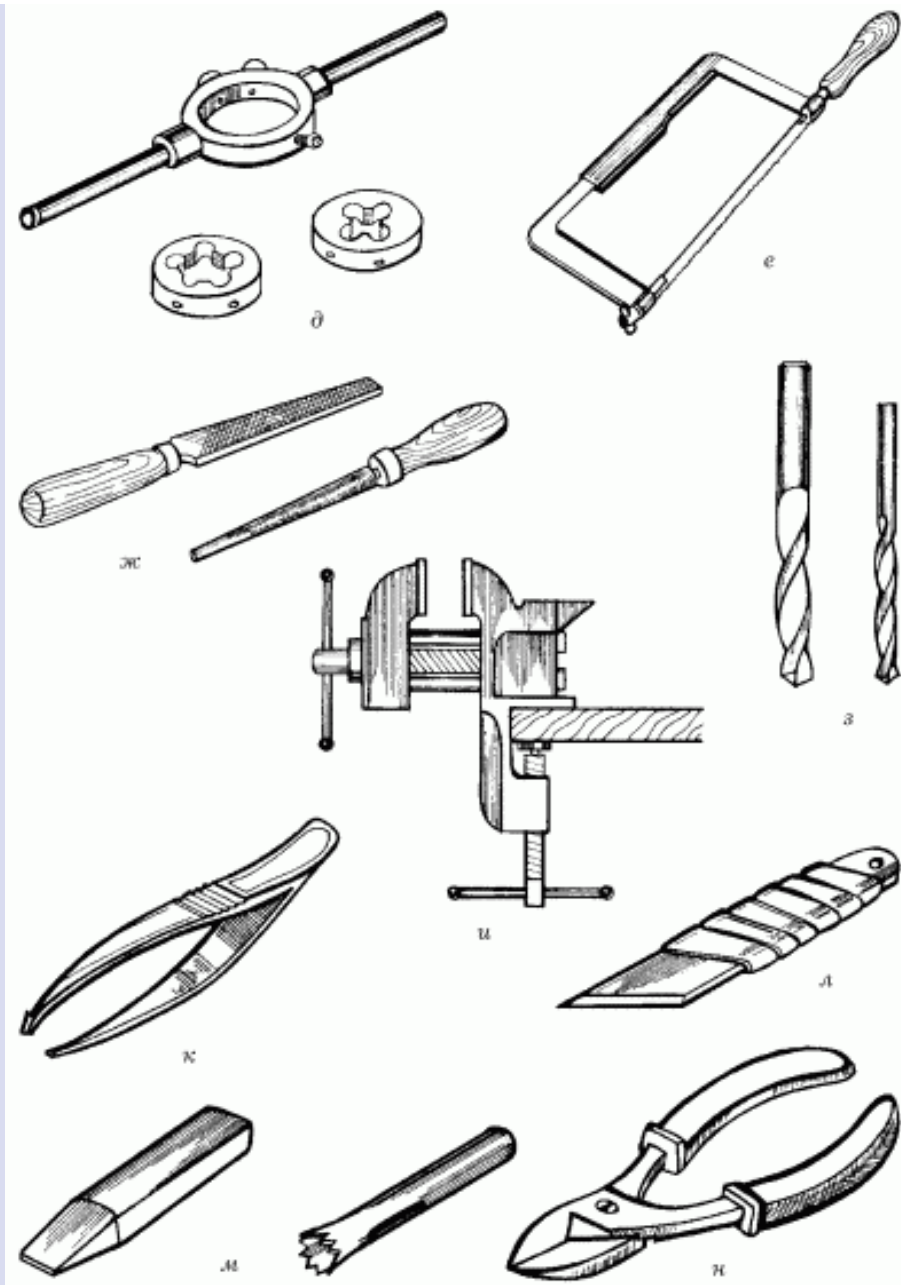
(продолжение): д – плашка с плашкодержателем; е – ножовка по металлу; ж – напильники; з – набор сверл; и – небольшие тиски; к – пинцет; л – монтажный нож; м – зубило и шлямбур; н – бокорезы с изолированными ручками.
